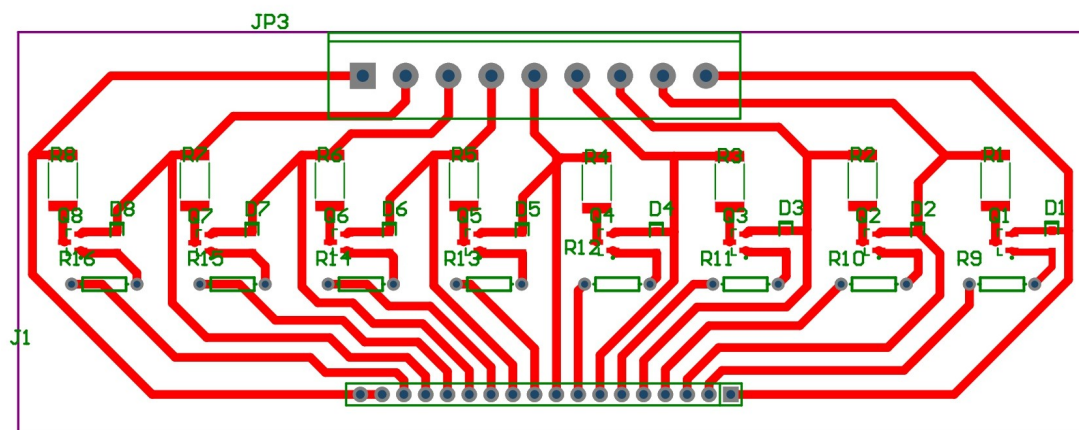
Diseño del PCB del circuito de balanceo externo
